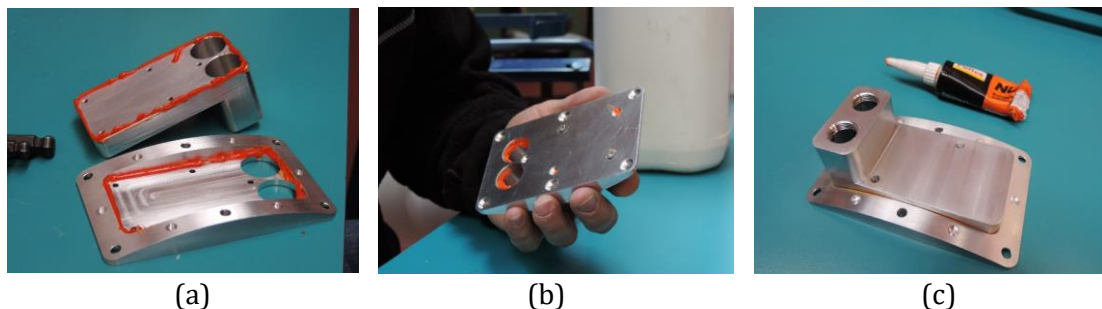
(a) Adición del sustituto universal de juntas en las piezas del soporte, (b) atornillado y eliminación de material sobrante (c) resultado final del soporte.
